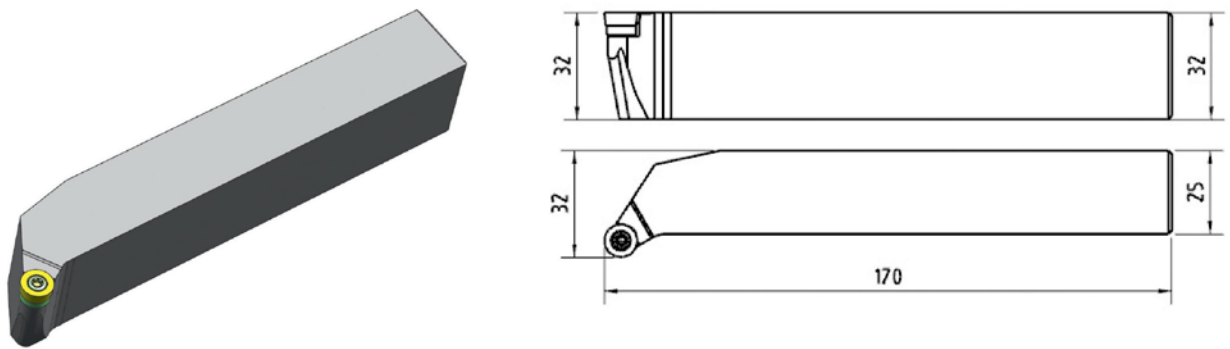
резец Sandvik для наружной обработки 301 102112R2
